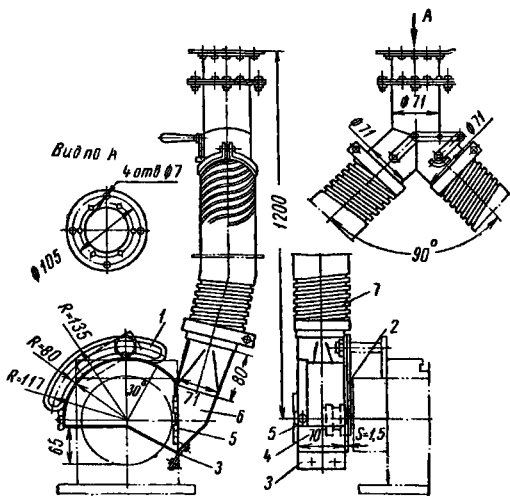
Защитно-обеспыливающий кожух универсально-заточного станка модели ЗА-64
